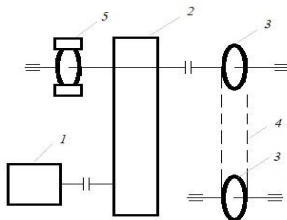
Кинематическая схема приводного механизма роторного паркинга
